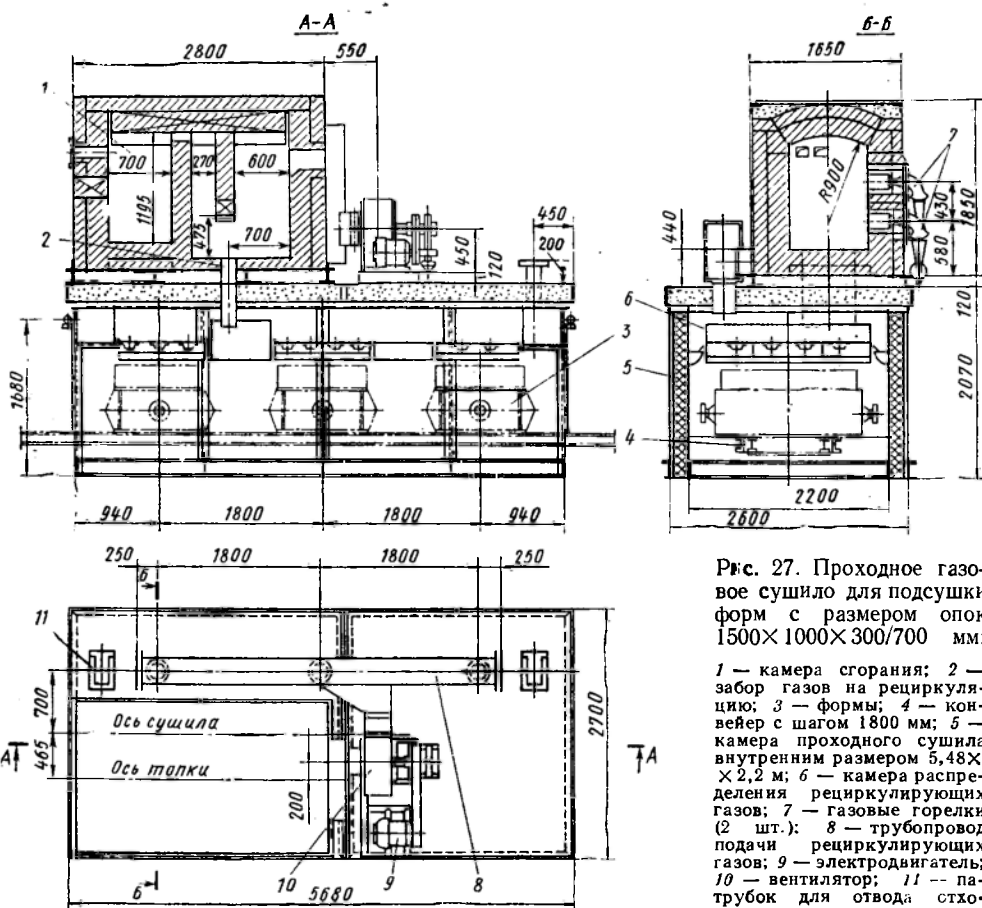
Проходное газовое сушило для подсушки форм с размером опок 1500×1000×300/700 мм:
